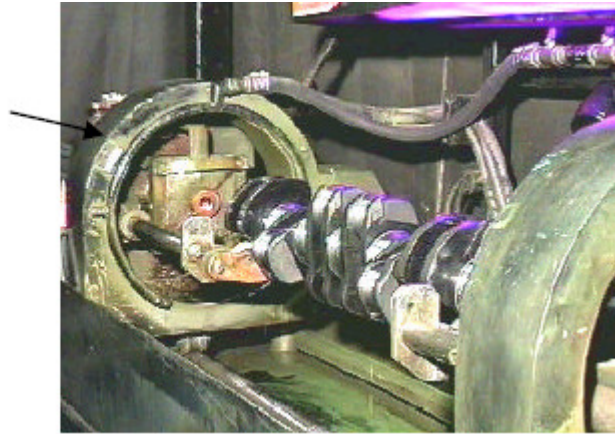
Ensaio de um virabrequim pela técnica da bobina
